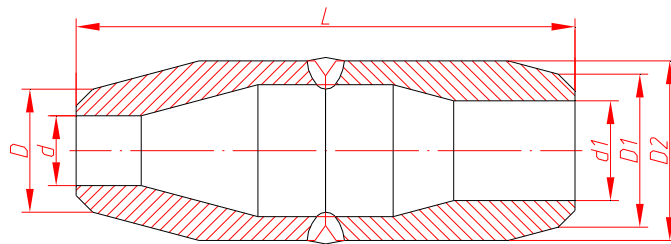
Переход сварной типа ...-ПС-НУ-... Общий вид
